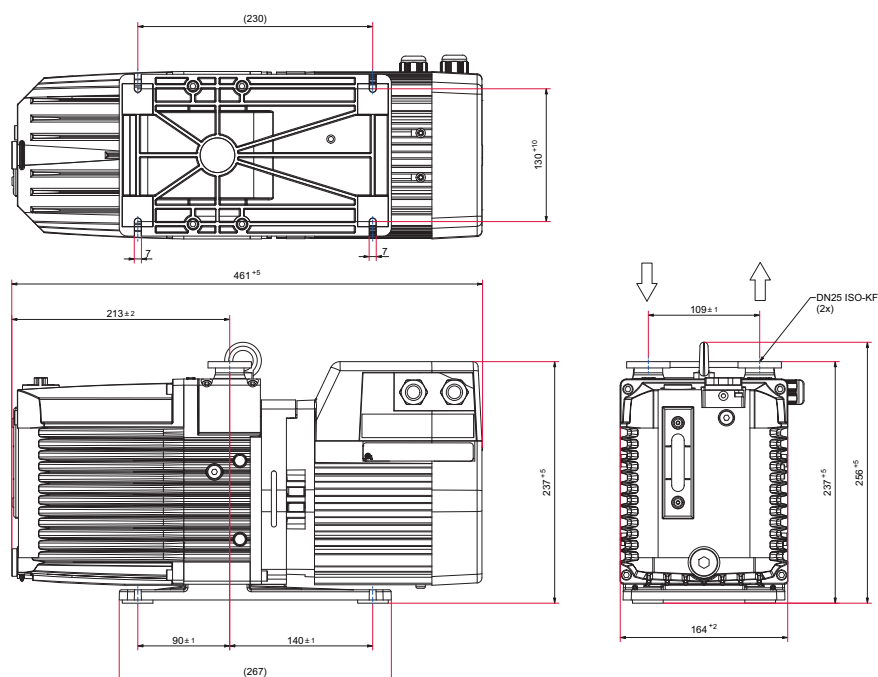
Dimensions DuoVane 22 avec moteur triphasé
